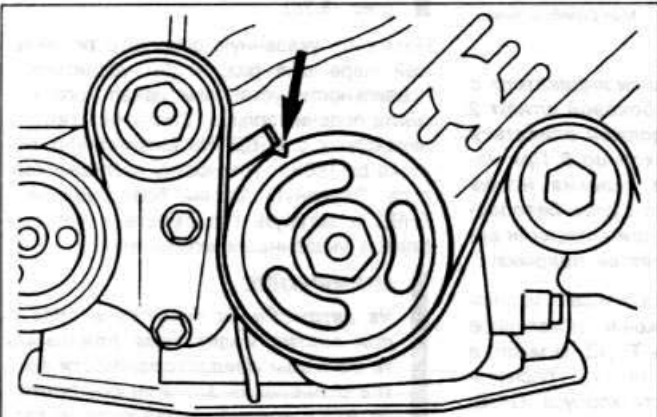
Совмещение меток на шкиве коленчатого вала и на блоке цилиндров
